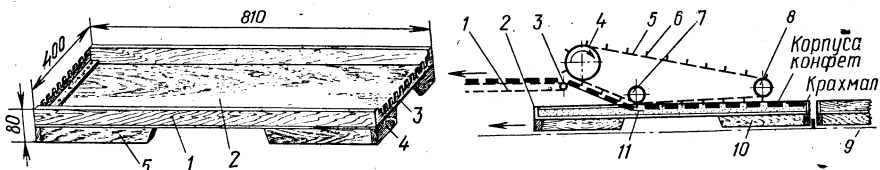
Лоток для механизированной отливки и выборки корпусов конфет:
